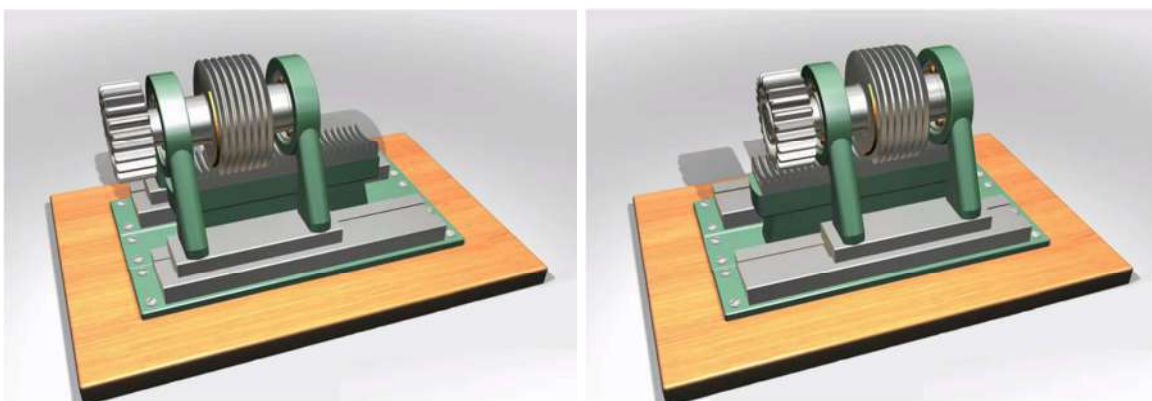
3D-модель черв'ячно-рейкової передачі (рейка не рухома)
